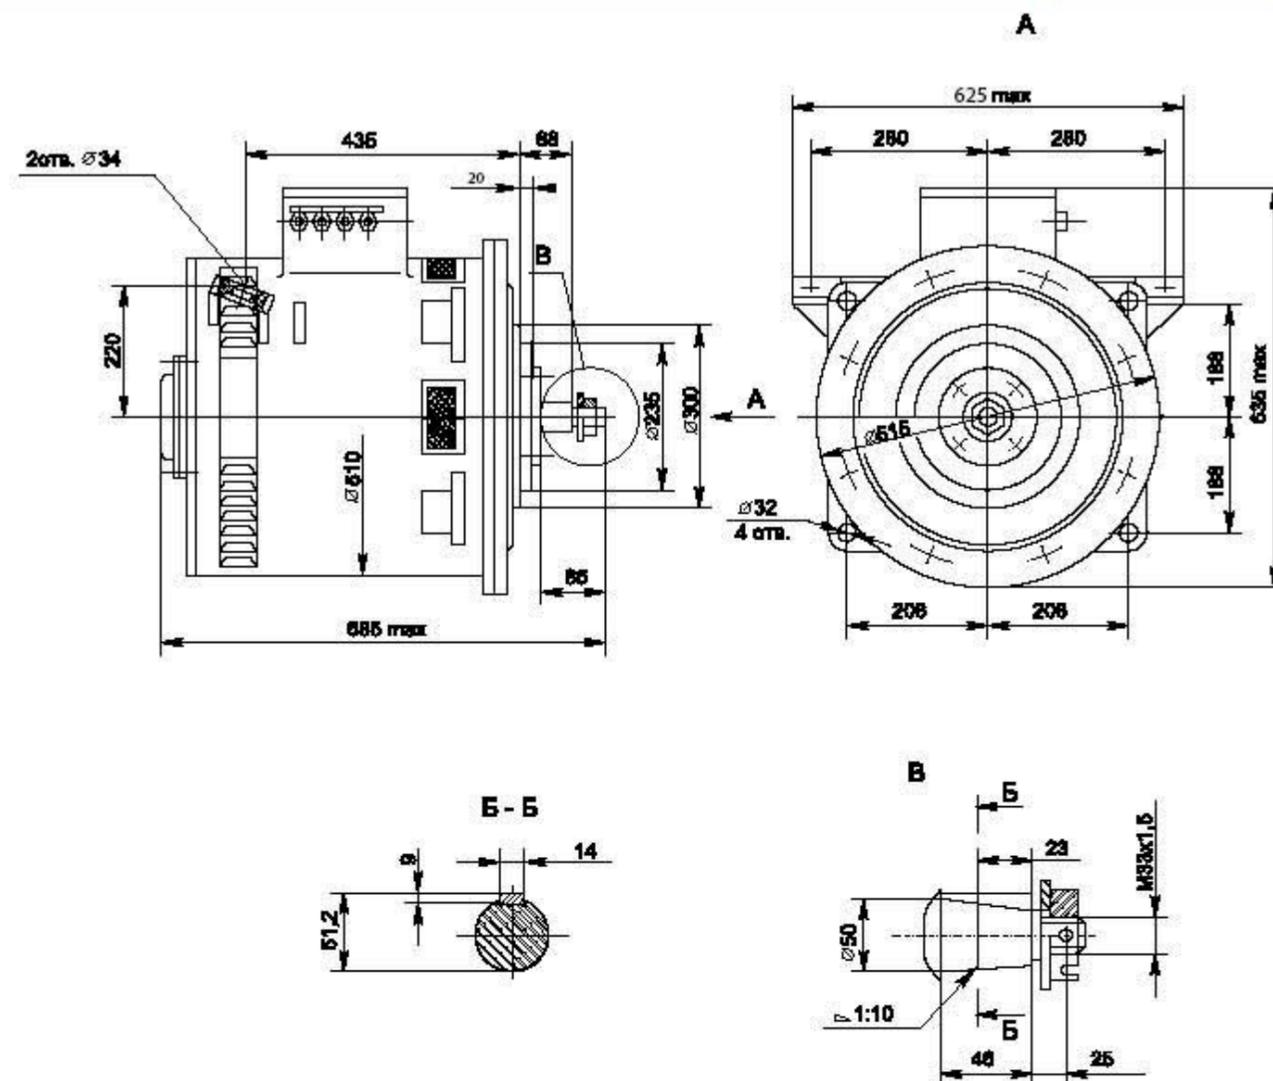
Габаритные и установочные размеры электродвигателя ДТН-34/25М
